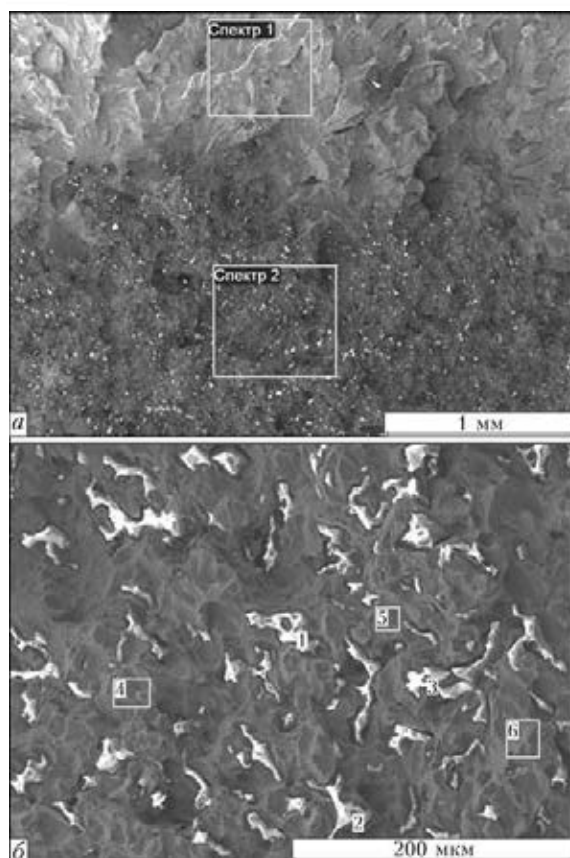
Матовые пятна на поверхности излома сварного соединения рельсов
